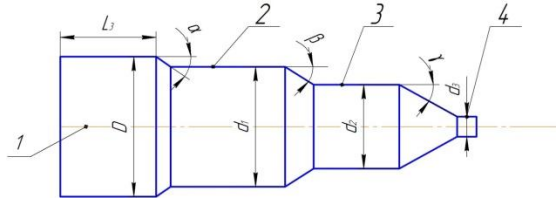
Эскиз ассиметричной детали с диаметрами ступеней  $d_1, d_2, d_3$ , получаемой скоростным выдавливанием из исходной цилиндрической заготовки диаметром  $D$  и длиной  $L_3$
